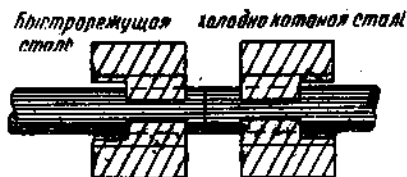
Зажим быстрорежущей стали, навариваемой на прутки стали обыкновенной.
